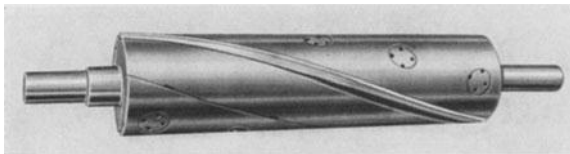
b. Schraubenförmige Messer einer Hobelmaschine.
